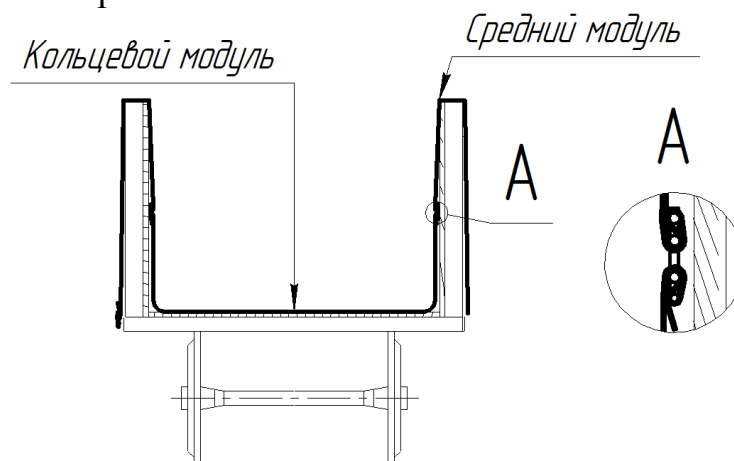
Размещение креплений МВ КТБ4в 7,0/6000-6000.
